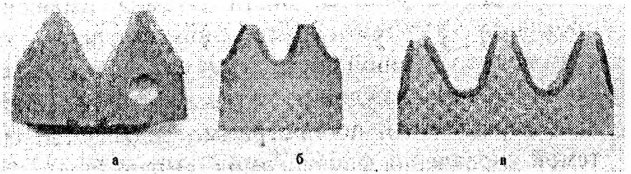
Расположение зоны закалки в сечении зубчатой поверхности шестерен колесной передачи: а - автомобиля МАЗ, б - автомобиля МЗКТ, в, - трактора МТЗ
